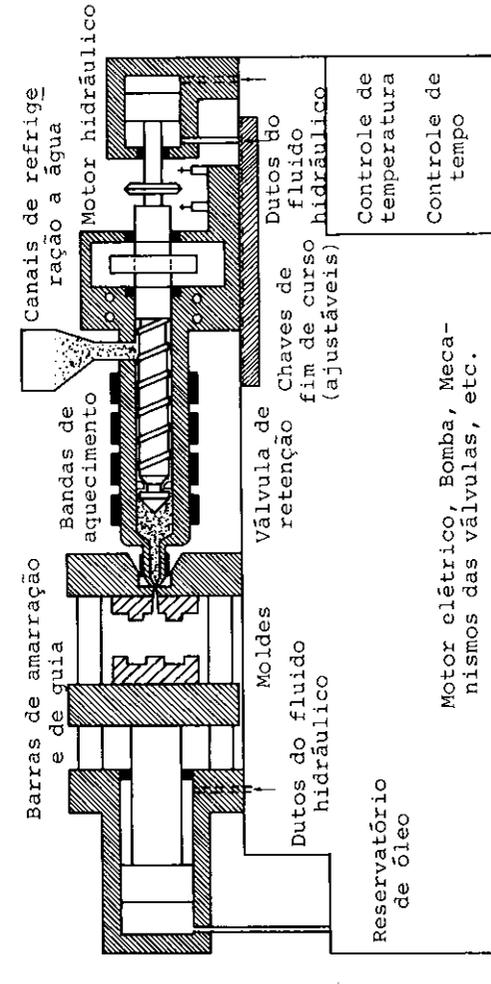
Máquina simples de moldagem por injeção de parafuso.
